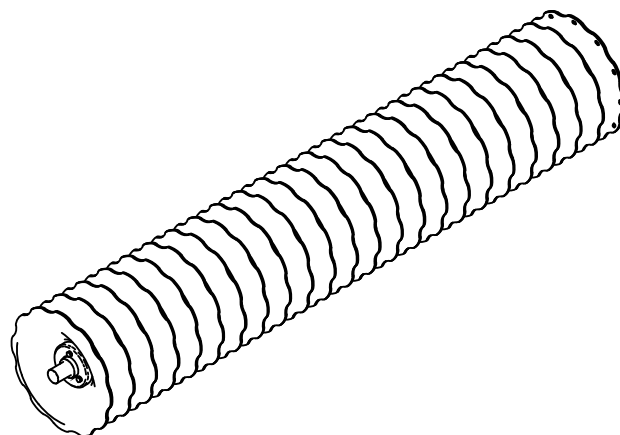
CrossCutter (Carrier 925–1225)
